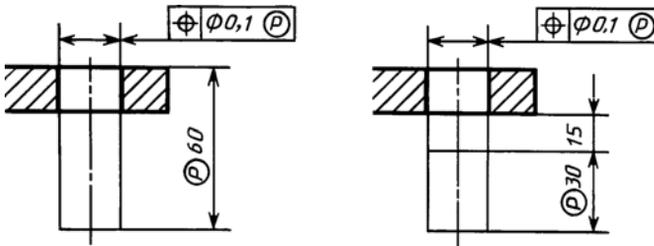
Обозначение допуска, если необходимо задать выступающее поле допуска расположения
